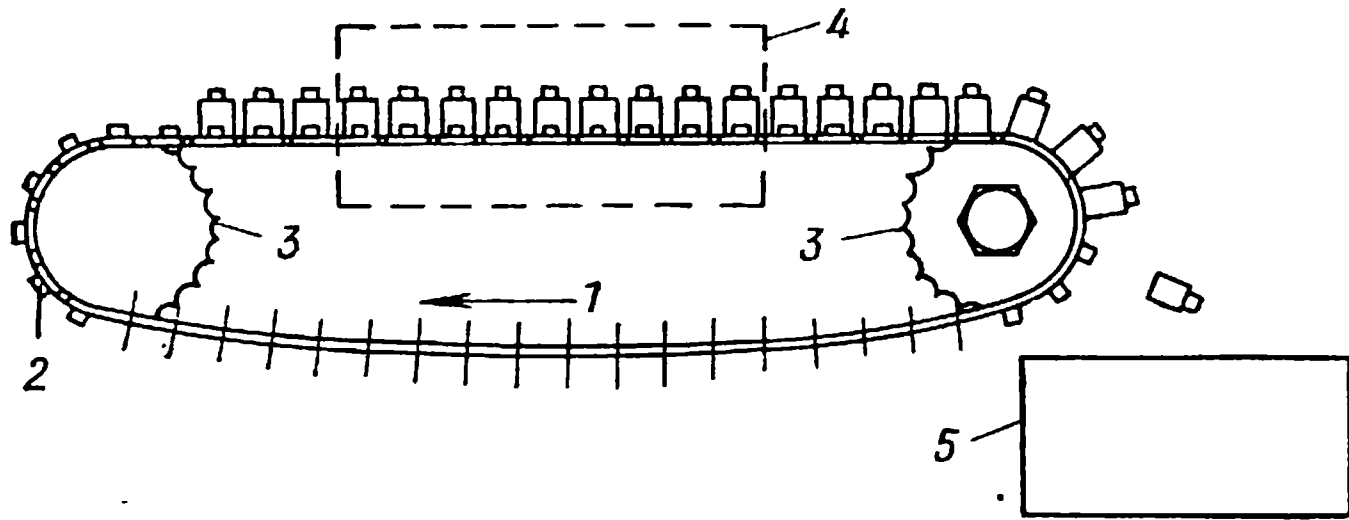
Схема установки конвейерного типа для газопламенной пайки
